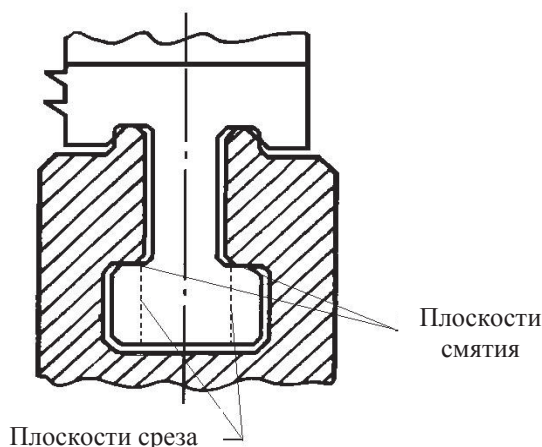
Т-образный хвостовик рабочей лопатки турбомшины, испытывающий срез и смятие
